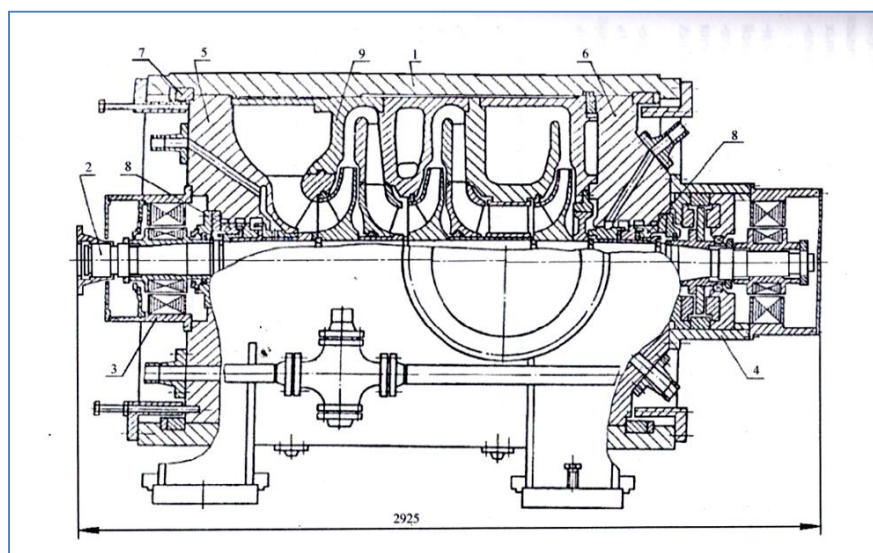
Полнонапорный трёхступенчатый нагнетатель НЦ-16 с электромагнитными подшипниками и «сухими» газодинамическими уплотнениями:
